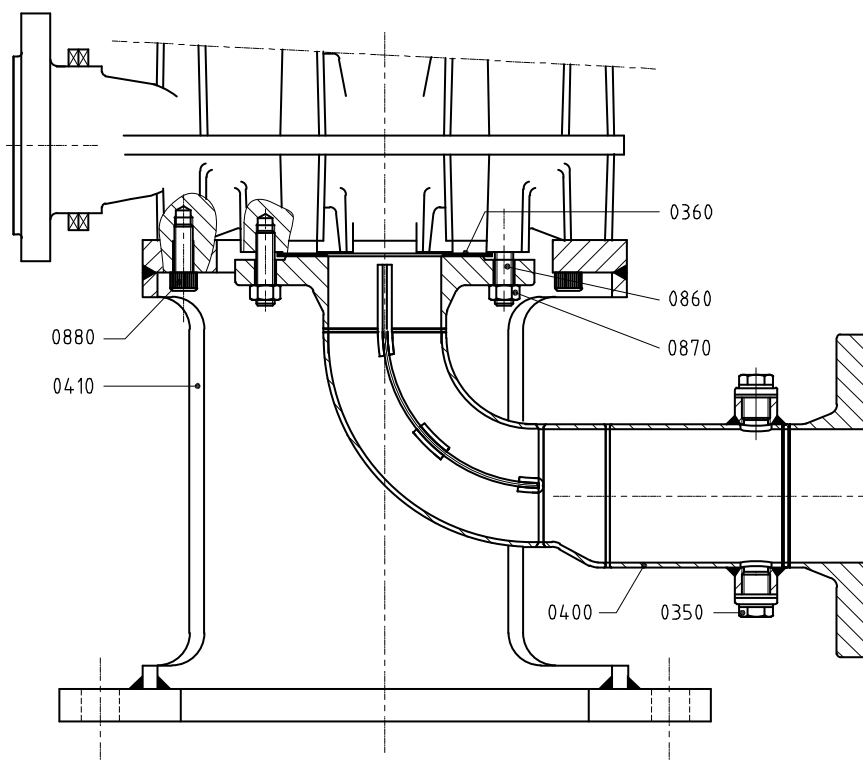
Чертеж в разрезе приемный патрубок 200–200 / 250В–315.
